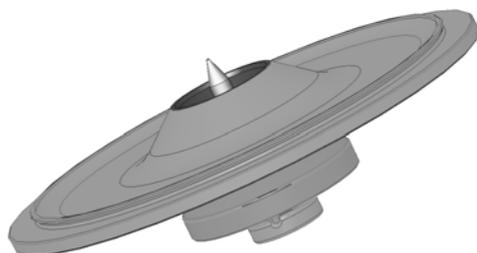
AutoLock™ Couvercle pour un rotor étanche aux aérosols
